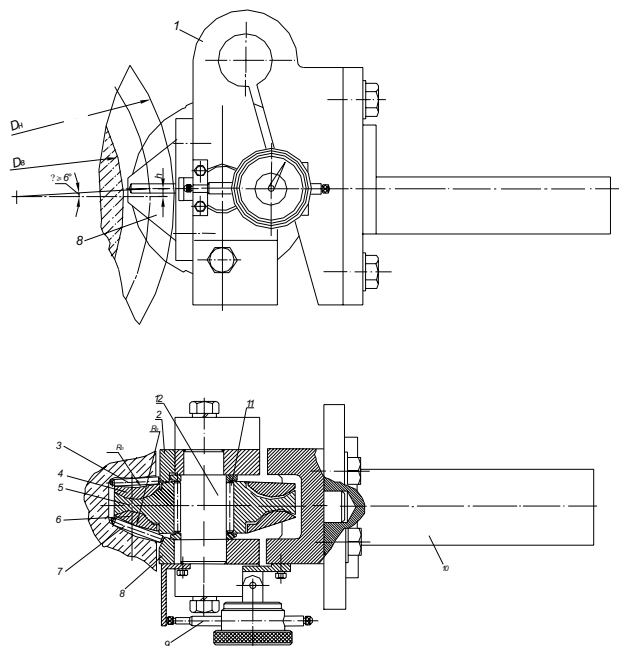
Схема устройства для обкатывания игольчатыми роликами упорной резьбы с шагом 64 мм
